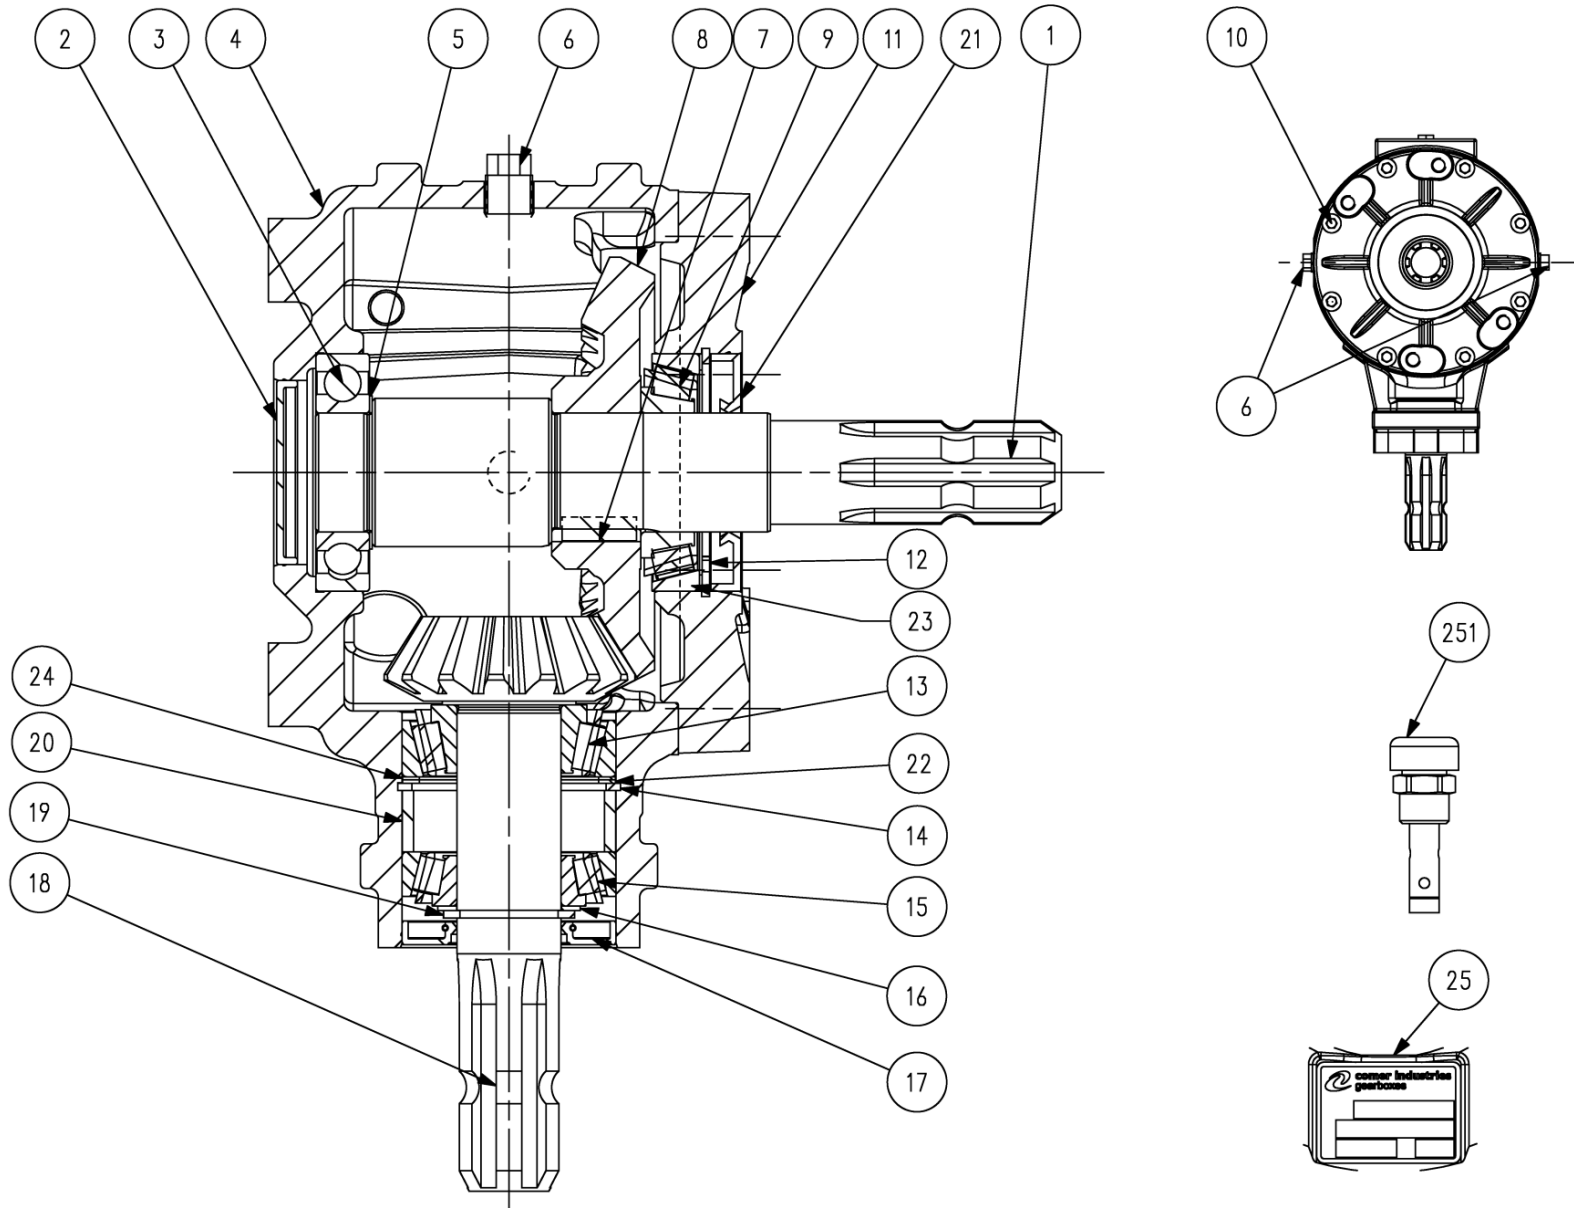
Редуктор 9.304.521.10 "Comer industries"
